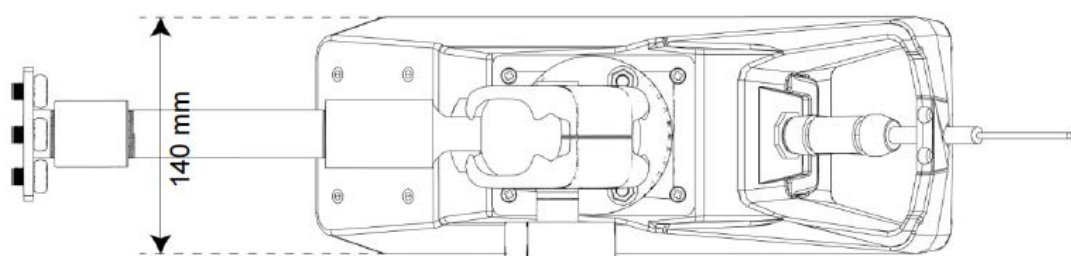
Vista en planta de las dimensiones del sensor RAVEN EYE según se ha instalado
